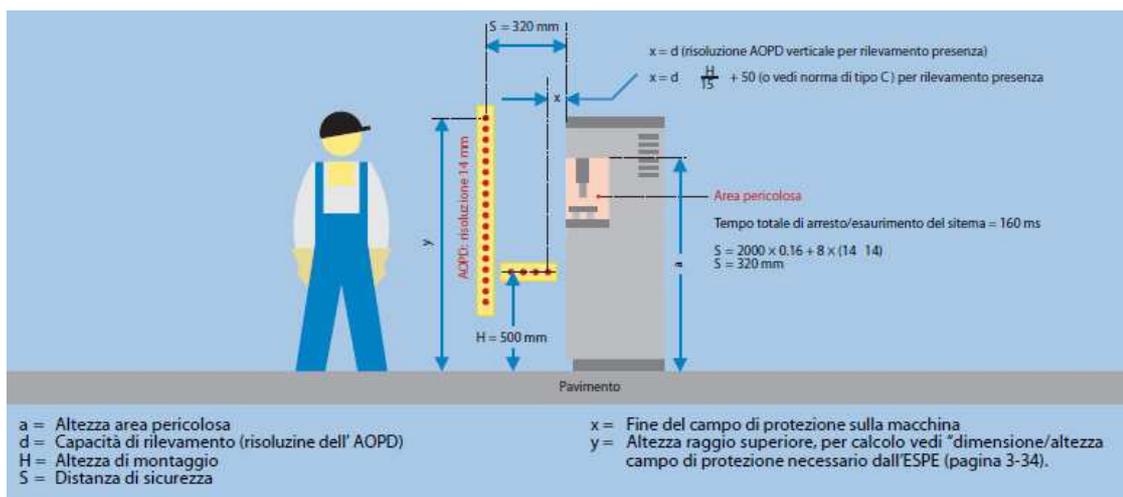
Distanza di sicurezza con protezione di barriera verticale e orizzontale. [9]
